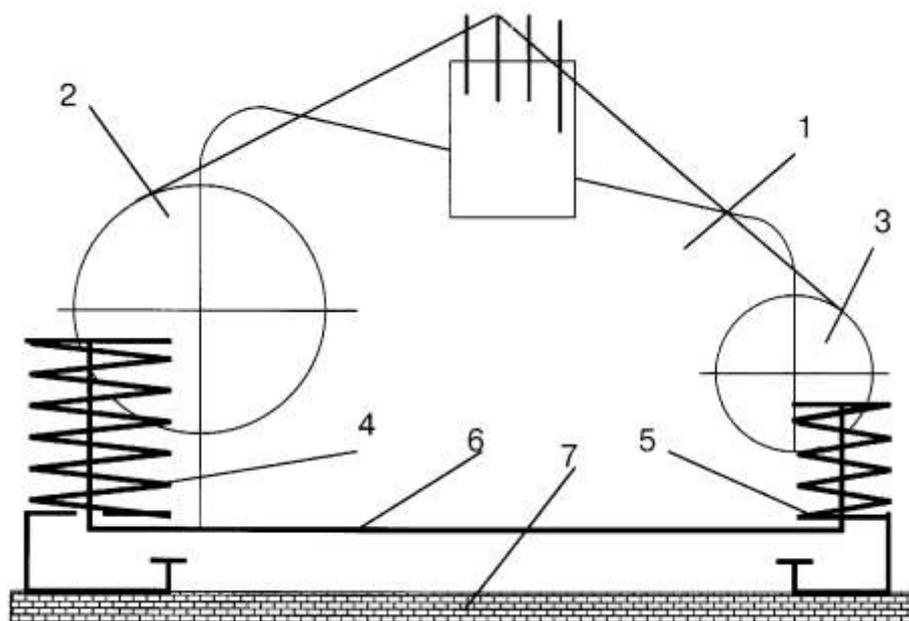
Расчетная схема системы виброизоляции для пневматических ткацких станков типа PN 130: 1–станок; 2–навой; 3–товарный валик; 4,5–резиновые виброизоляторы со стороны навоя станка и со стороны грудницы; 6–опорная поверхность станка; 7–межэтажное перекрытие.
